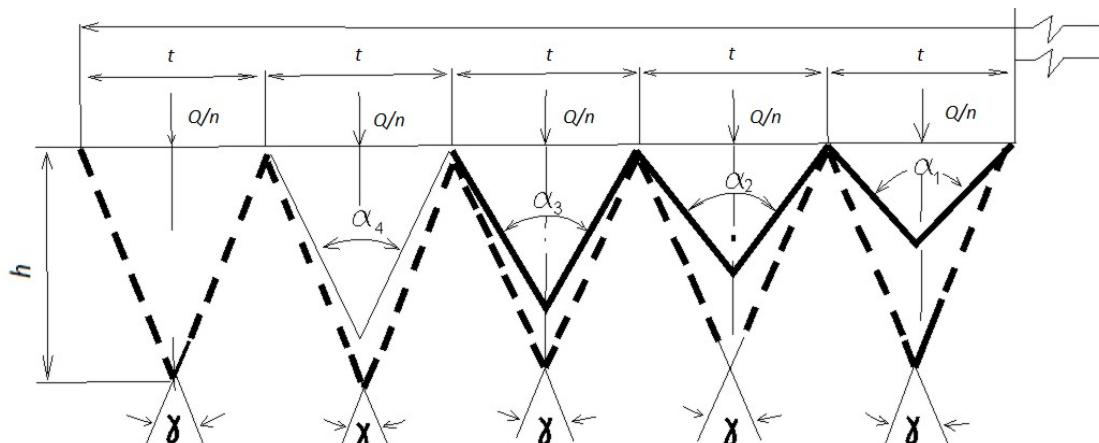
Схема гребешкового и равнонагруженного профиля торца коронки:
